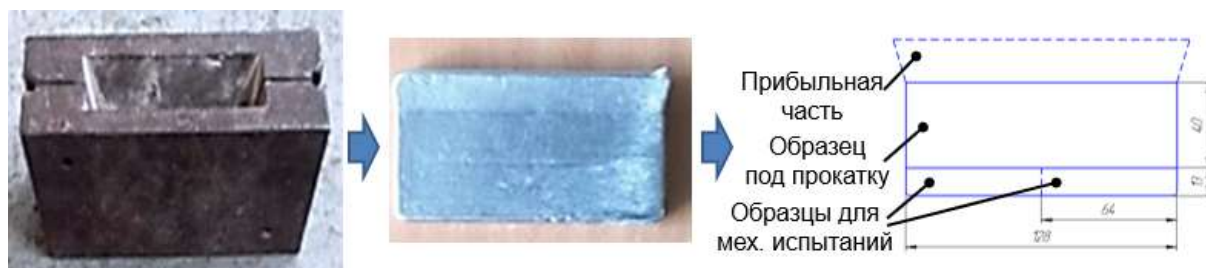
Внешний вид кокиля, отливки и схема разметки
